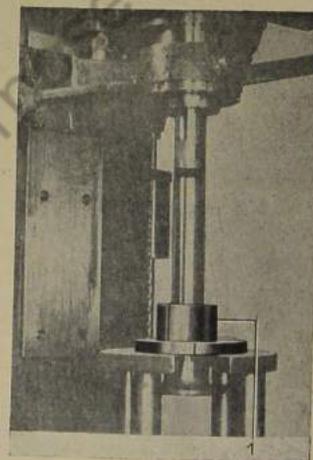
Laufbuchse zum Schrägrad für 4. Gang abpressen
